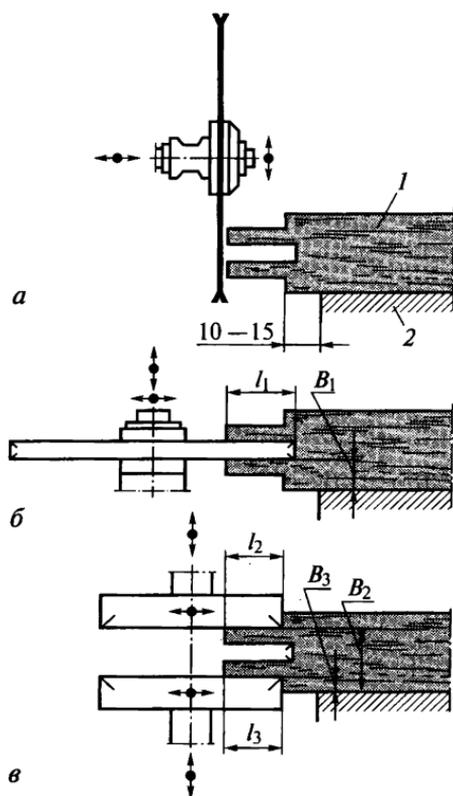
Настройка режущих инструментов одностороннего рамного шипорезного станка:
